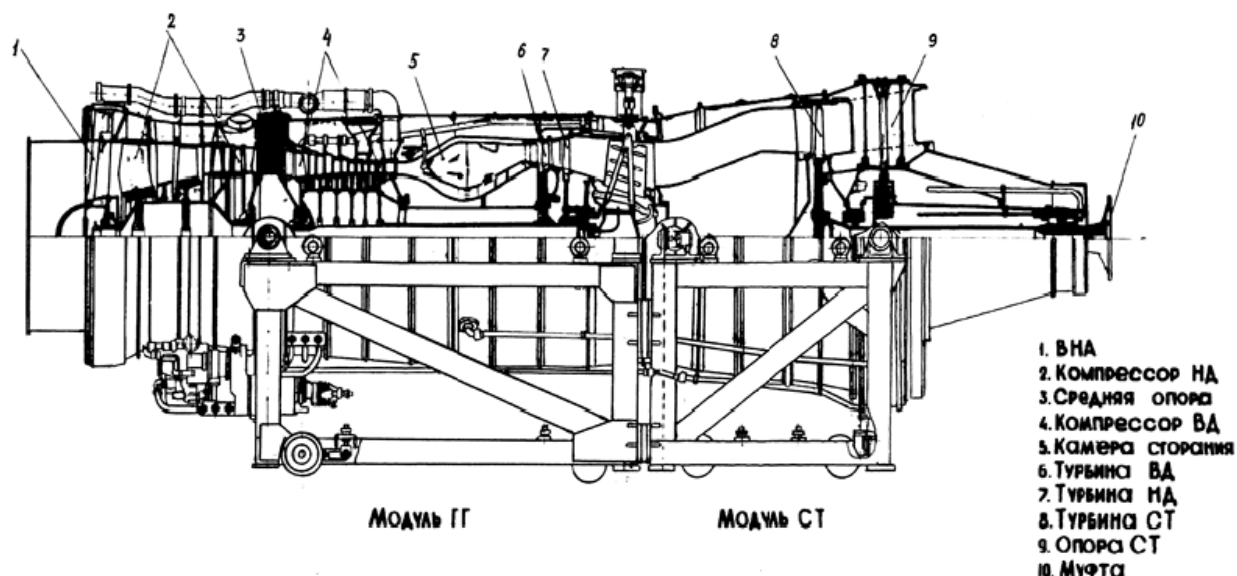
Газотурбинный двигатель НК-16СТ в разрезе.
